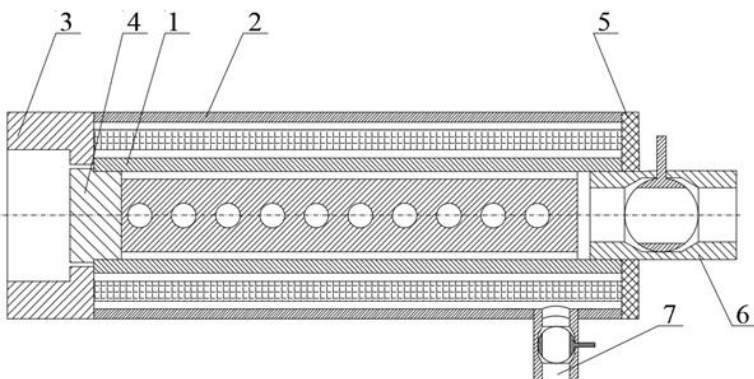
Теплова труба з акумулюванням теплоти: 1 – робочий корпус; 2 – вторинний корпус; 3 – мідна заглушка вторинного корпусу; 4 – мідна заглушка робочого корпусу; 5 – загальна заглушка теплової труби; 6 – клапан поповнення робочої рідини; 7 – клапан поповнення рідини з низькою температурою кипіння
